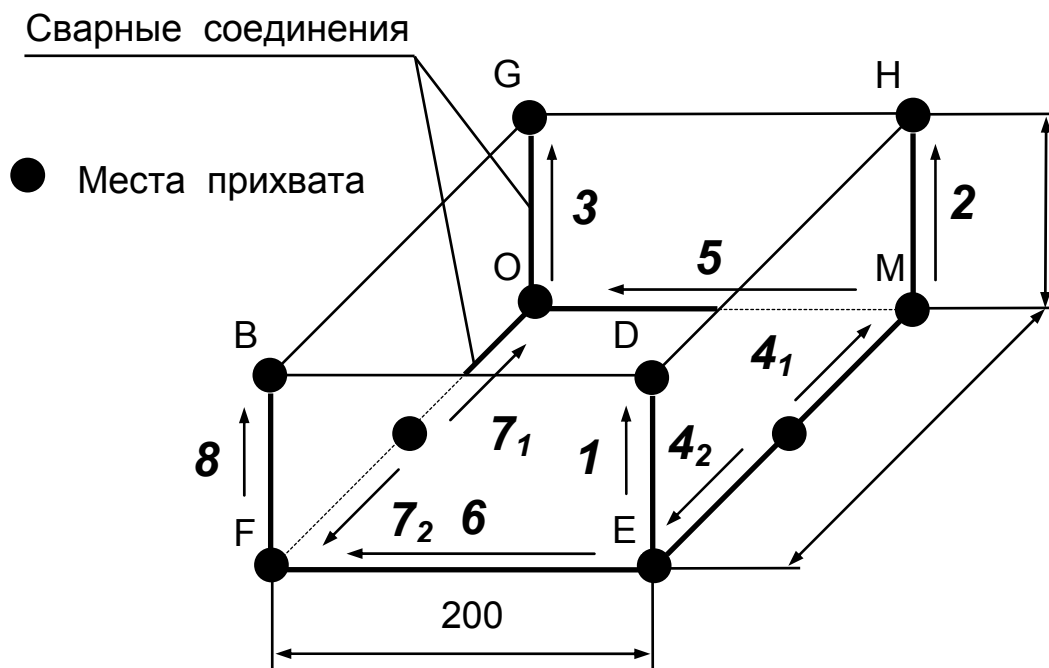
Эскиз металлической ванны с размерами: порядок наложения швов указан большими цифрами; последовательность — маленькими цифрами; направление сварки — стрелочкой
